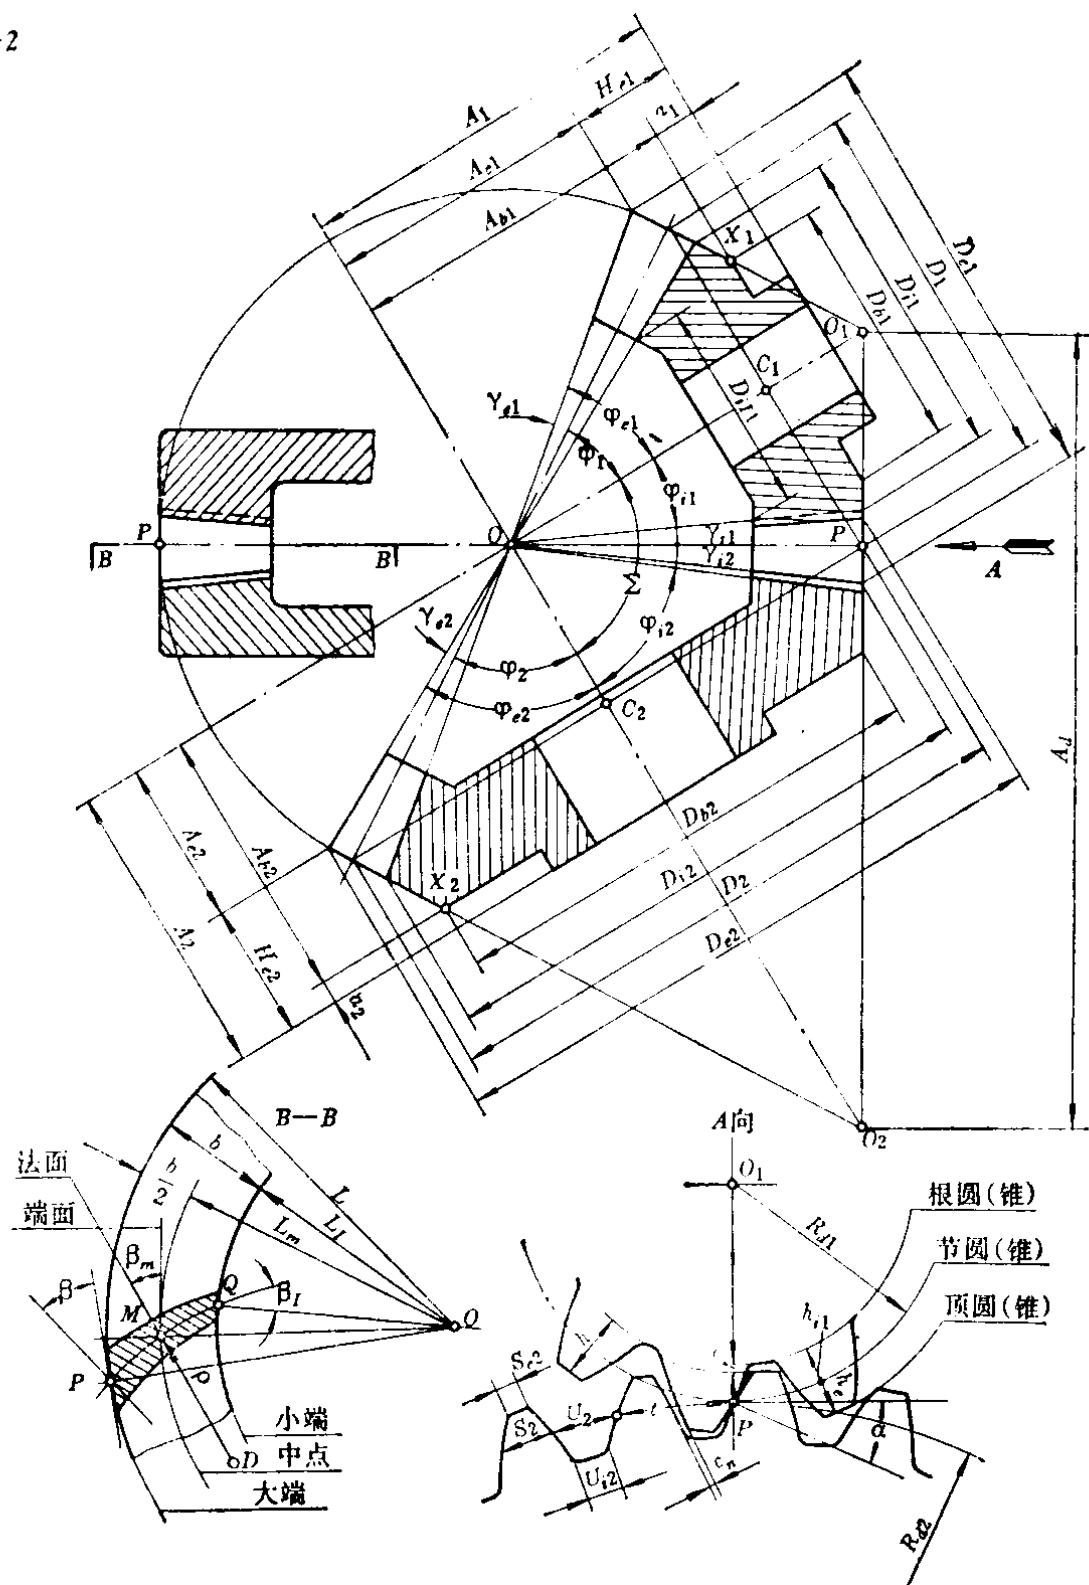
圆锥齿轮副的要素和各部位尺寸
